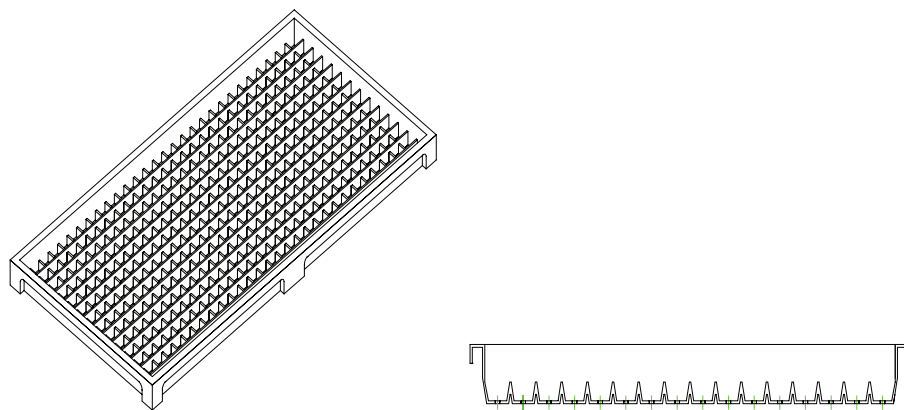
水稻钵形毯状秧盘平面图（左）和剖面图（右）
